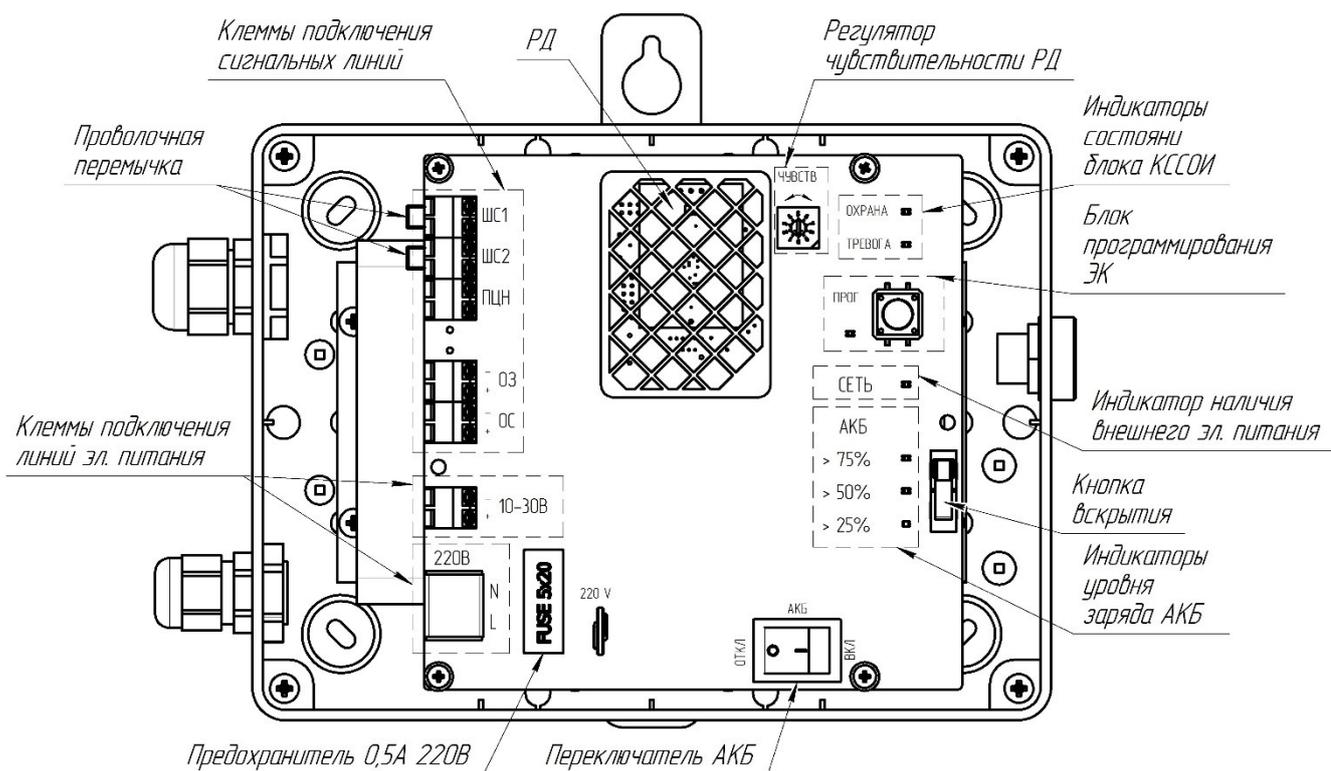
Внешний вид блока КССОИ без крышки
